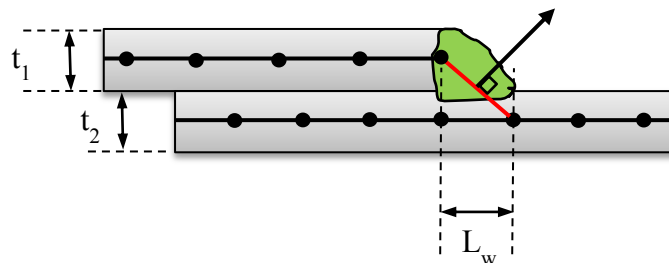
Elementos para soldadura sobrepuesta.
